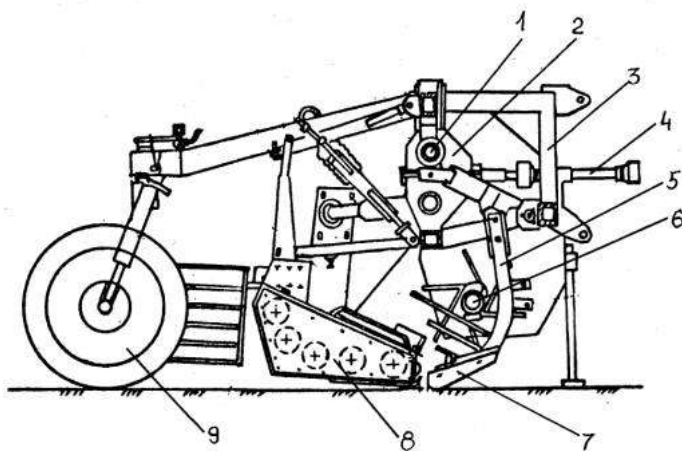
Конструктивна схема навісної машини КВЦБ-1,2 з лемішними віброкопачами [19]: 1 – ексцентриковий механізм; 2 – редуктор; 3 – рама; 4 – карданна передача; 5 – викопуючий пристрій; 6 – бітер-проштовхувач; 7 – лемеші; 8 – шнековий очищувач; 9 – опорні колеса.
